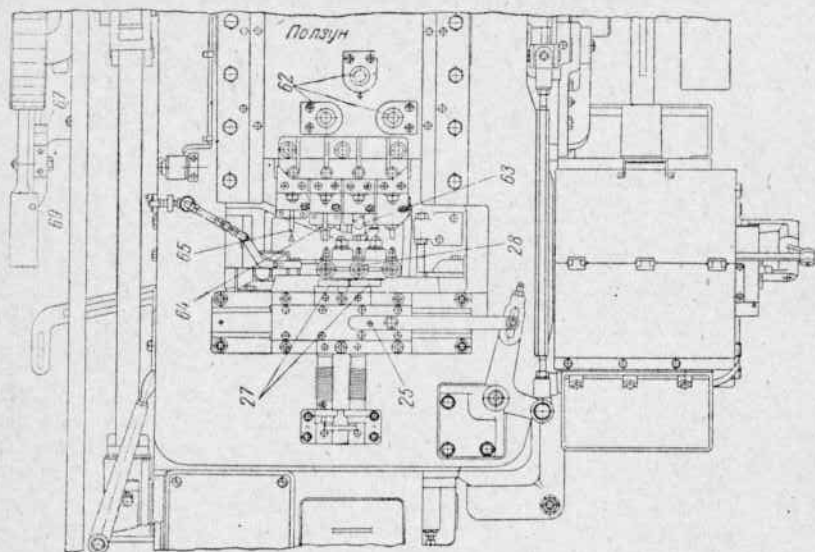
б. Общий вид гайковыводочного автомата диаметром 12 мм (вид со стороны механизма реза).
